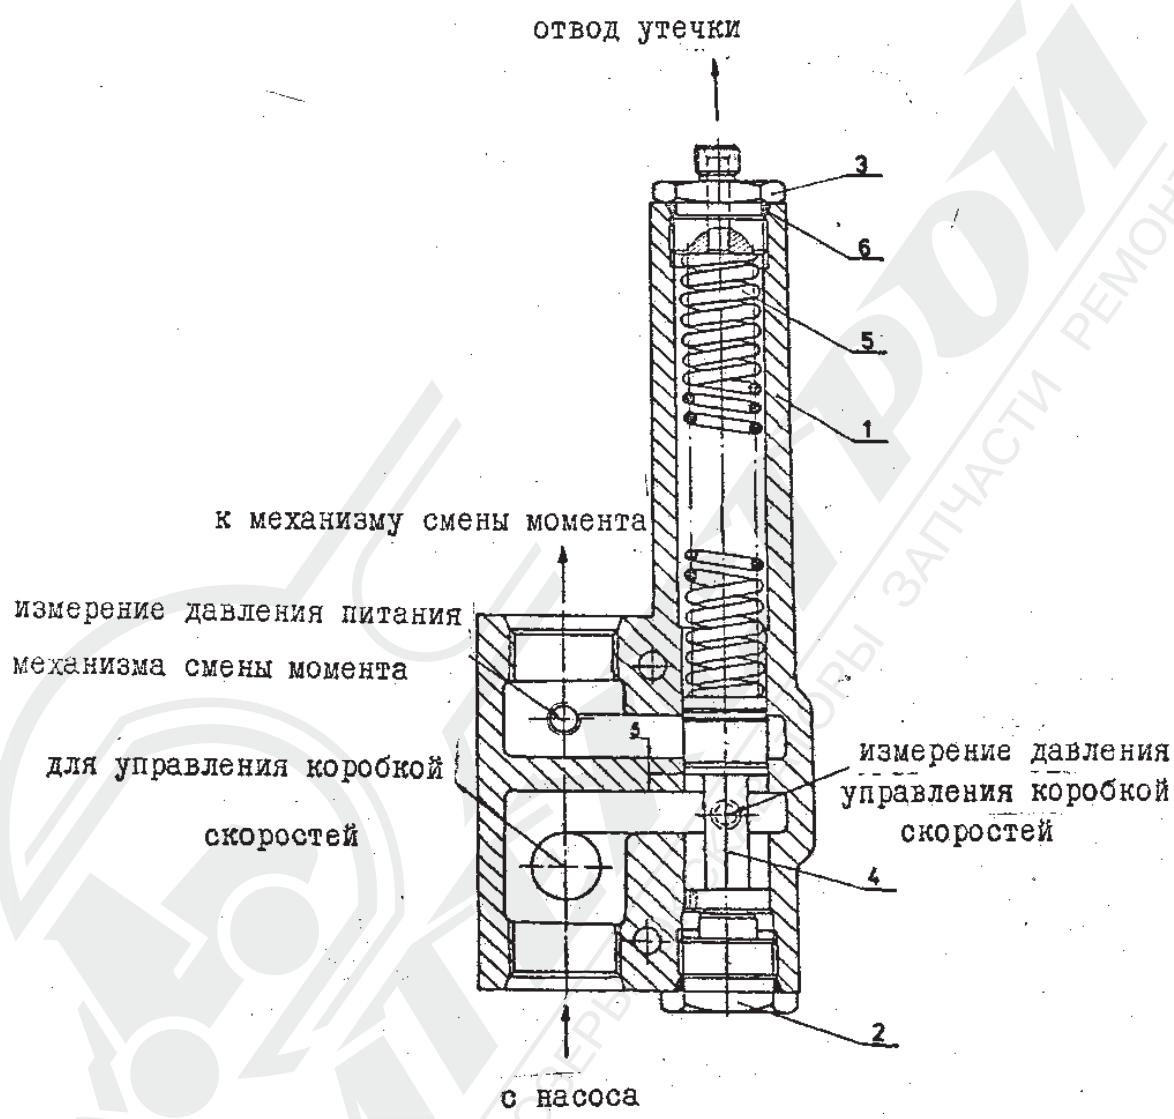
Поршневой клапан типа ZM151N-04-00
